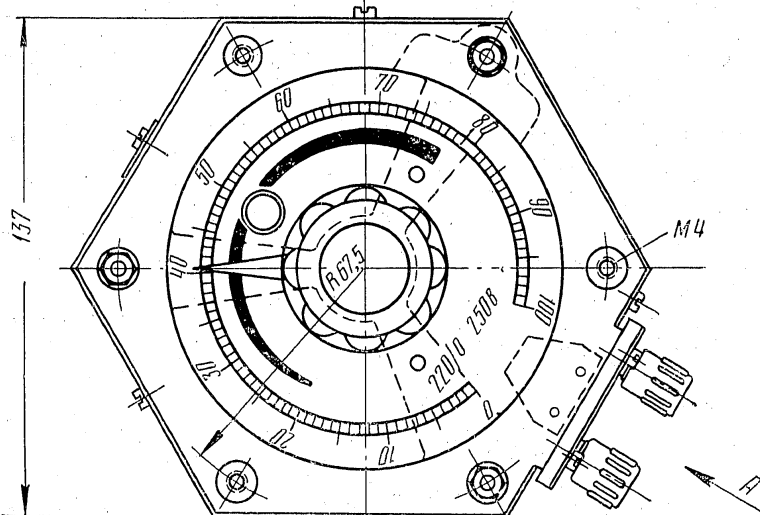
Конструкция однофазного вариатора РНО-250-0,5 на 0,5 кВа: 1—пластмассовая подушка 2—обмотка; 3—литорка; 4—роликовая щетка; 5—пластмассовое кольцо; 6—магнитопровод
